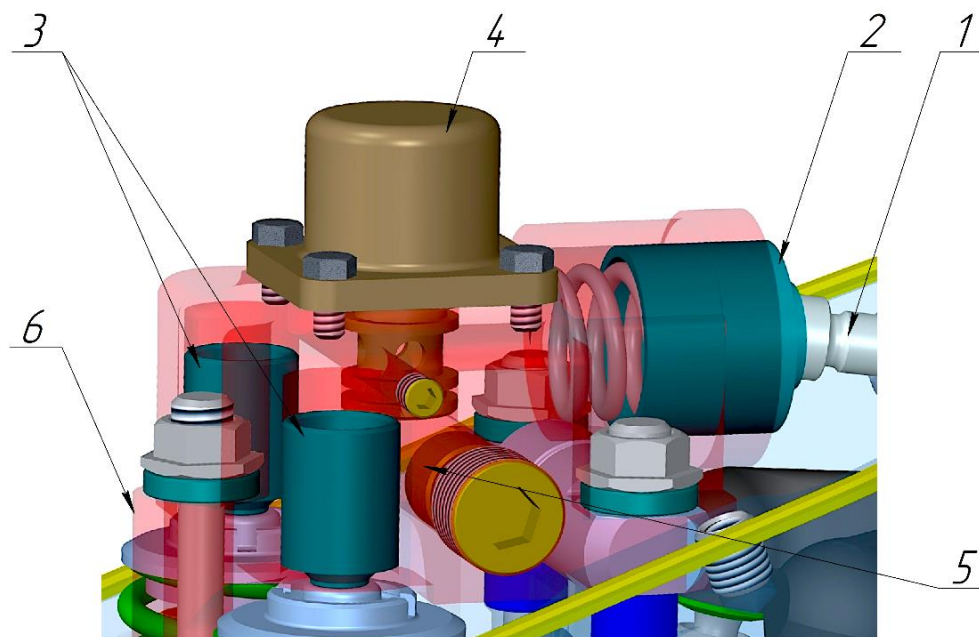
Твердотельная модель привода управления выпускными клапанами механизма газораспределения: 1 – штанга, 2 – насосный блок, 3 – камеры высокого давления, 4 – электромагнитный клапан, 5 – аккумулятор давления, 6 – корпус
